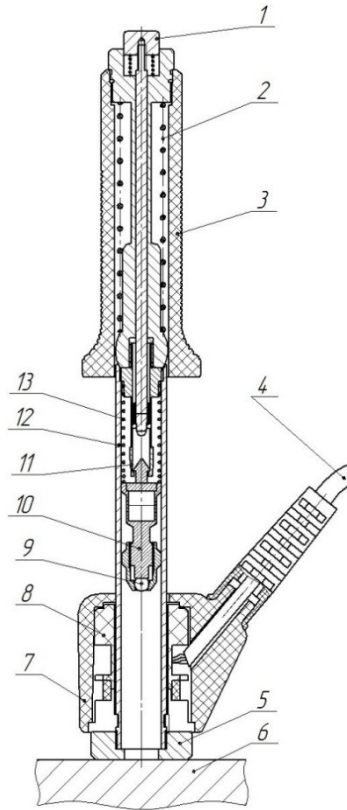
Схематическое изображение ударного преобразователя (Тип D) перед ударом (ударная пружина взведена): 1 – кнопка спуска; 2 – взводящая пружина; 3 – взводящая трубка; 4 – соединительный кабель; 5 – опорное кольцо; 6 – испытуемый образец; 7 – корпус катушки индуктивности; 8 – катушка индуктивности; 9 – сферический наконечник; 10 – ударник; 11 – цанга; 12 – направляющая трубка; 13 – ударная пружина
